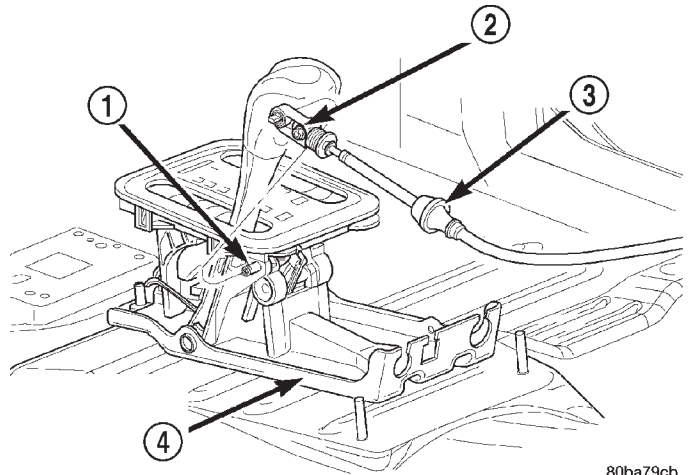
Cable de cambio de marcha de la transmisión en el cambiador
